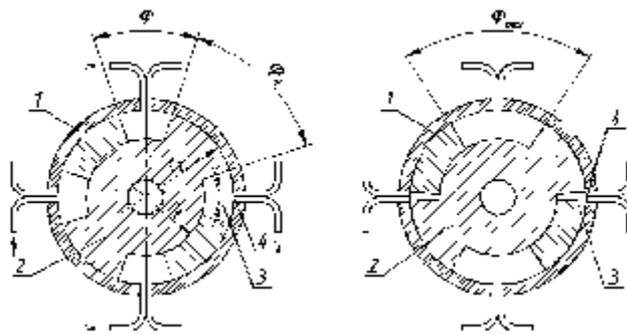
Схема работы четырехкамерного роторно-лопастного компрессора
